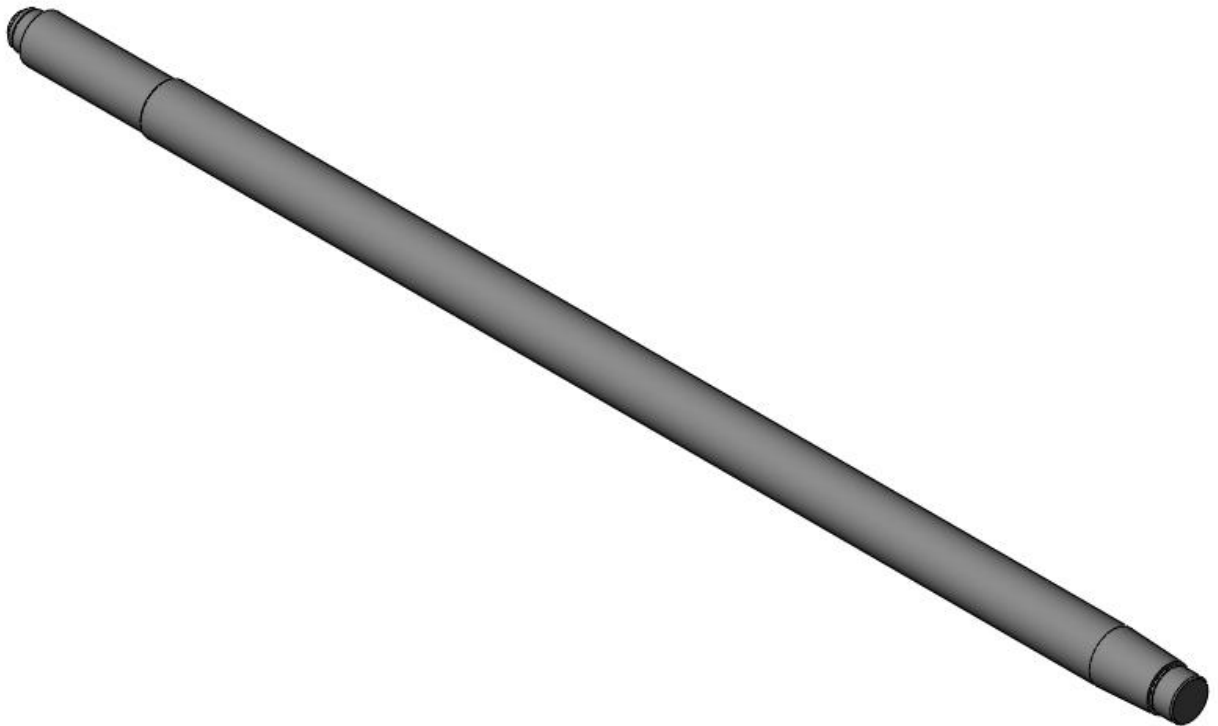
Твердотільна модель вала верхнього вальця
